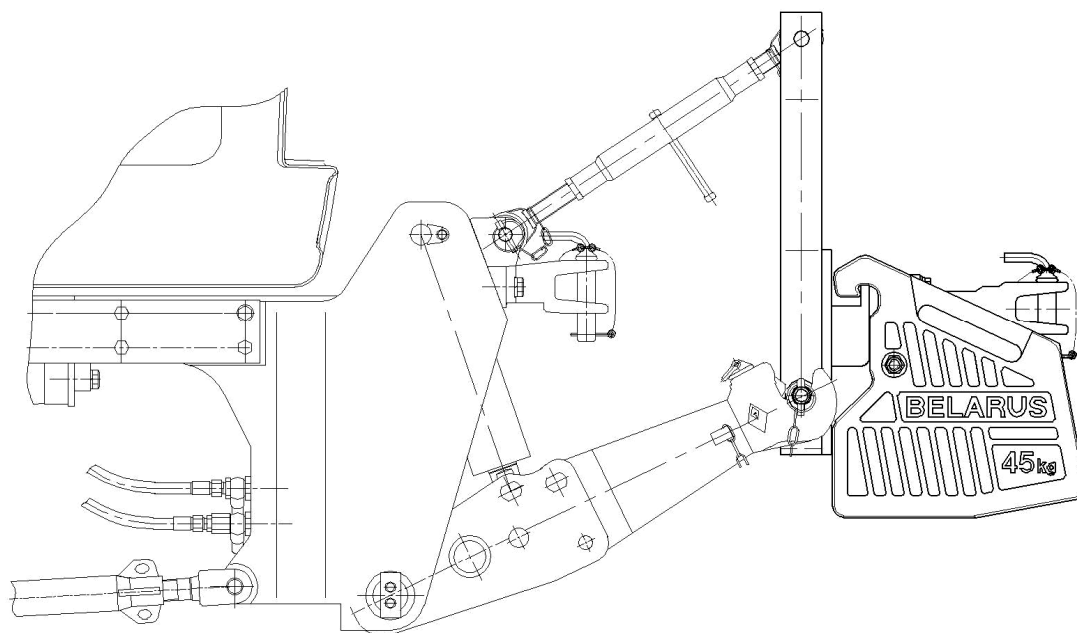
Схема установки навесных балластных грузов на ПНУ
